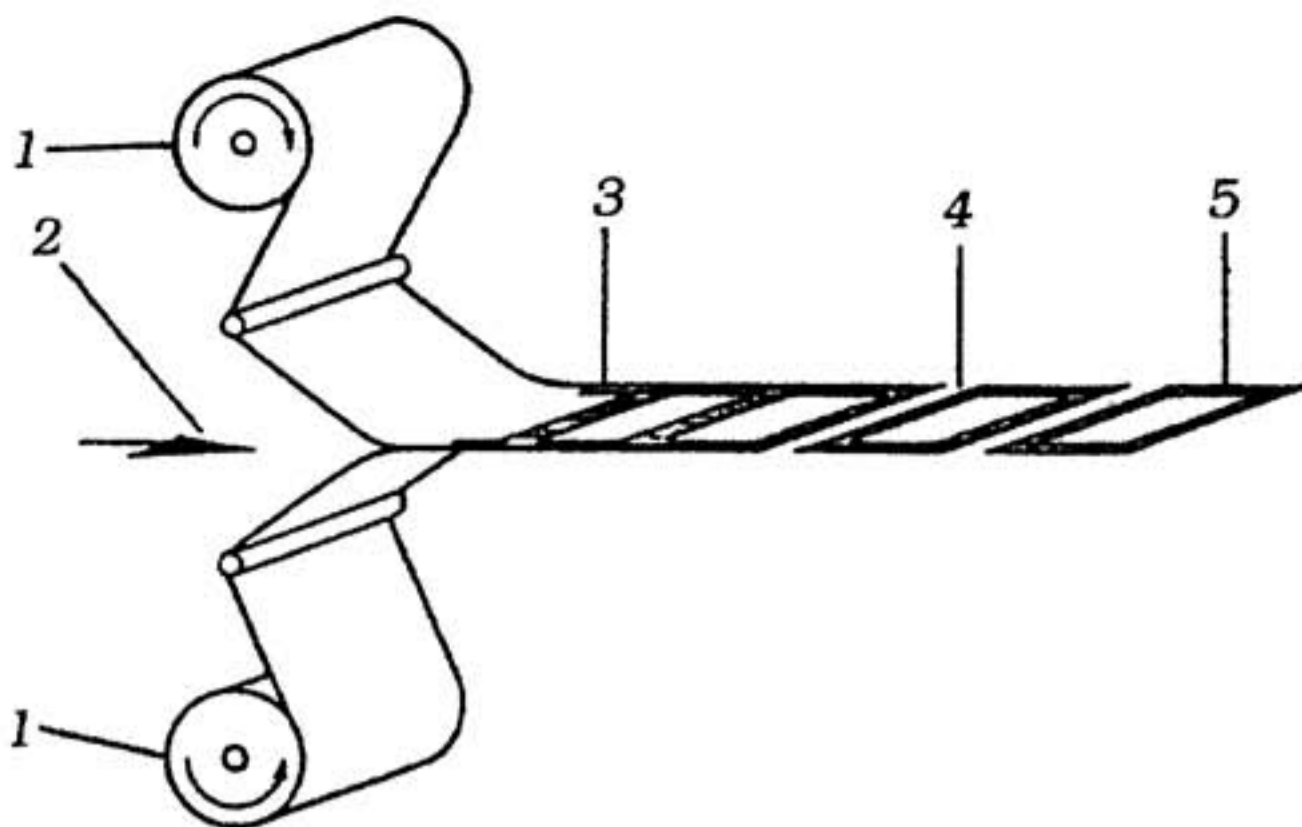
Схема способа изготовления мягкой тары на упаковочном автомате горизонтального типа с одного рулона: 1 — рулон пленки; 2 — упаковываемый продукт; 3 — сварка продольного шва; 4 — сварка поперечного шва и отрезка; 5 — упаковка
